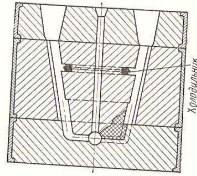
Отливка конуса камнедробилки в разрезе. Вес обработанной отливки 4000 кг; вес залитой стали 4700 кг.
